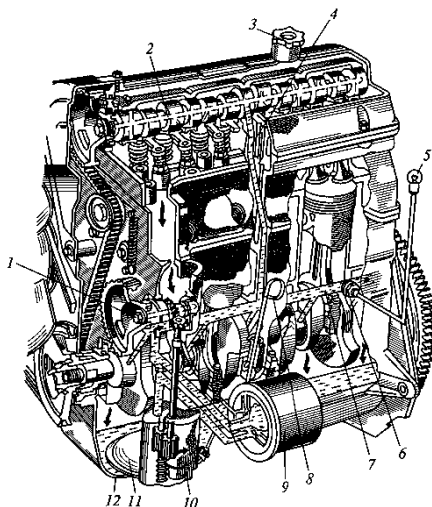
Смазочная система двигателя легкового автомобиля:
